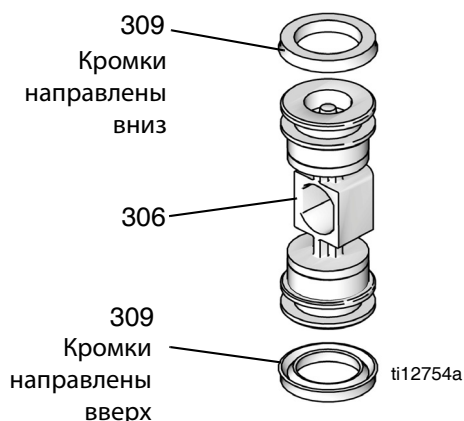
Установка уплотнения П-образного сечения в воздушный клапан
